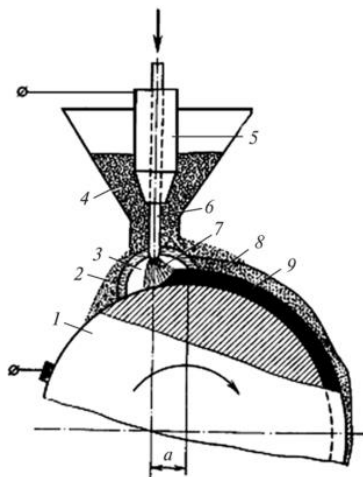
Автоматическая сварка и наплавка под слоем флюса
